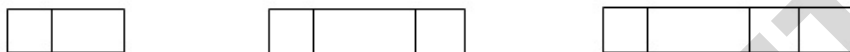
Рамки для обозначения допусков формы и расположения поверхностей
